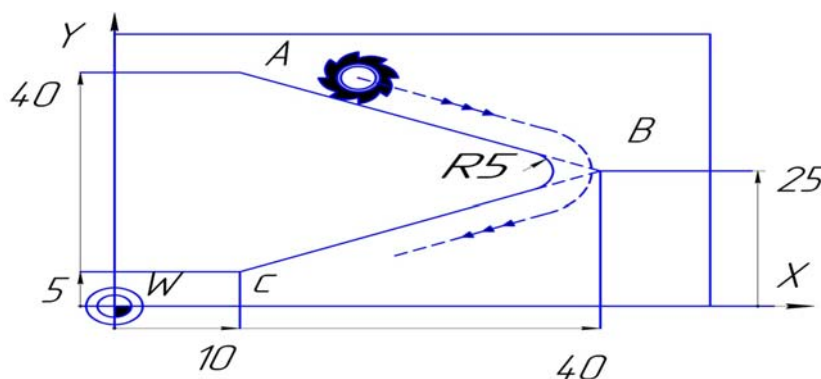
Закругление углов обрабатываемого контура заготовки
